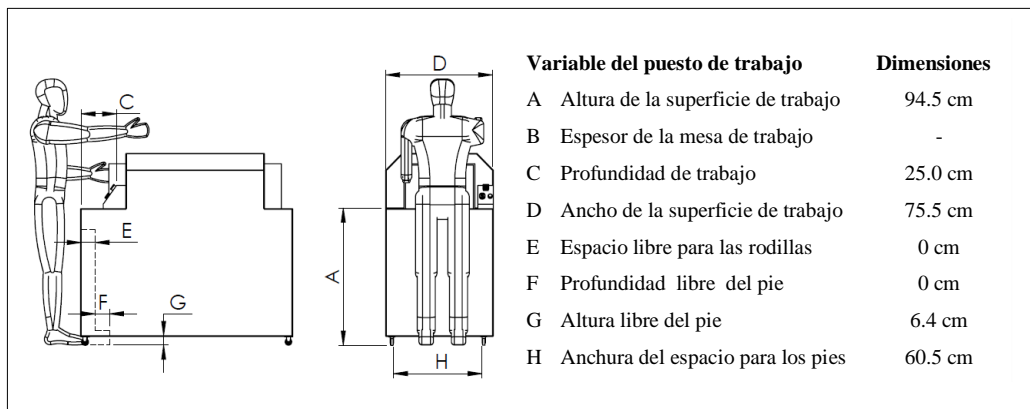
Dimensiones actuales del puesto de enfriado zapato
